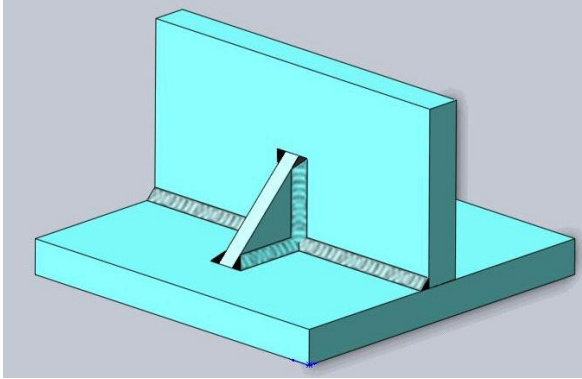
Готова деталь зі зварним тавровим з'єднанням
